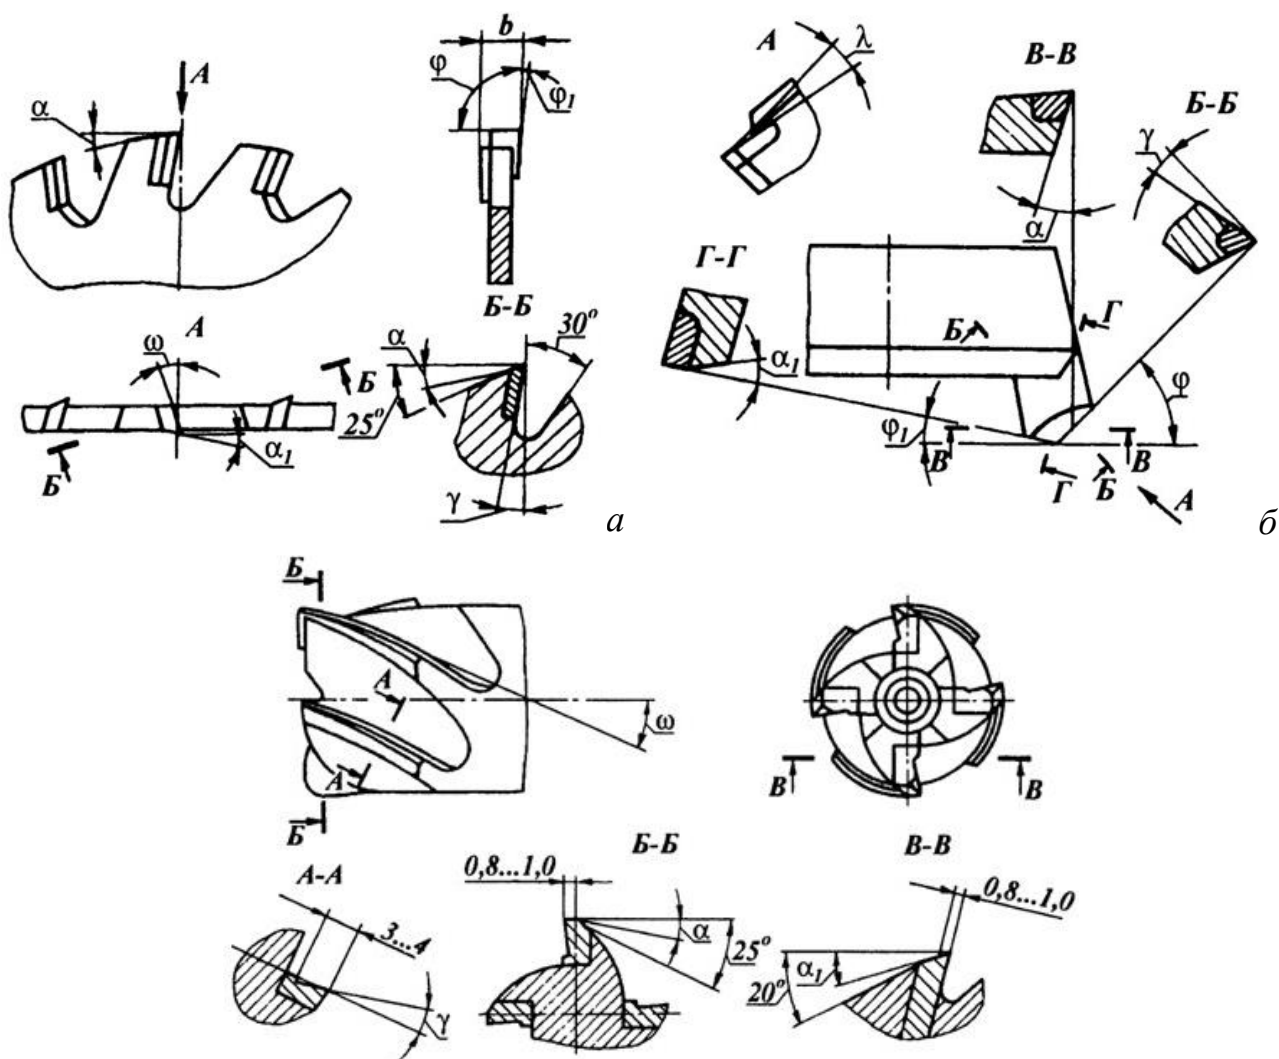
дискова (а), торцева (б) й кінцева (в) фрези для обробки пластмас.
